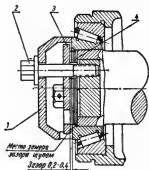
Проверка осевого зазора в коническом роликовом подшипнике конечной передачи тракторов ДТ-54, ДТ-54А с помощью приспособления:
